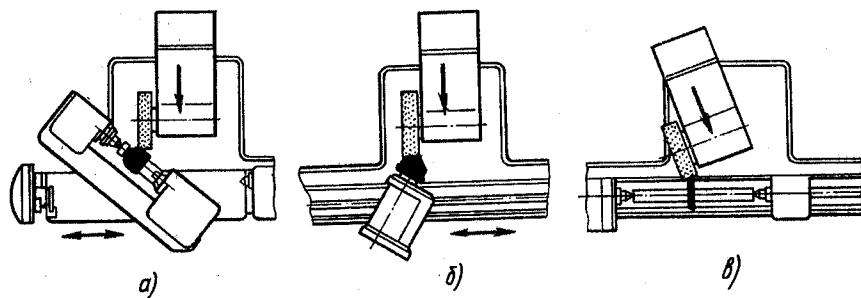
Схема наладки станка для шлифования поверхности с большой конусностью
